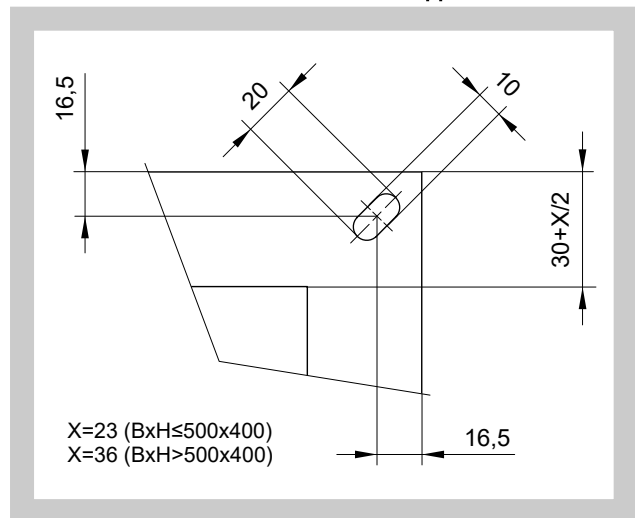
Flanschanschluss der Klappe – EINBAUSEITE
